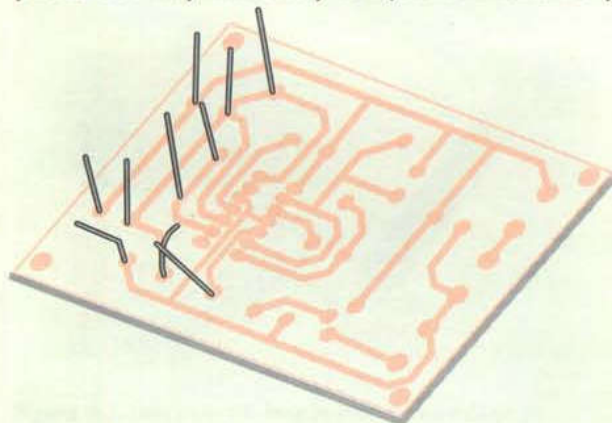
Montaje de algunos componentes para su soldadura
